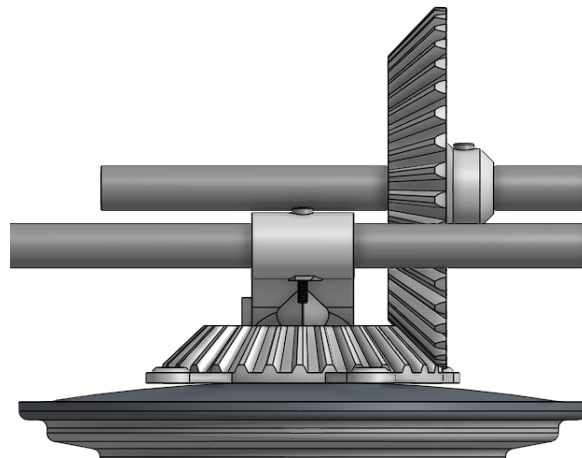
Vista isométrica 1 del ensamblaje de la transmisión con engranajes cónicos con el alternador en Onshape [fuente: elaboración propia]
